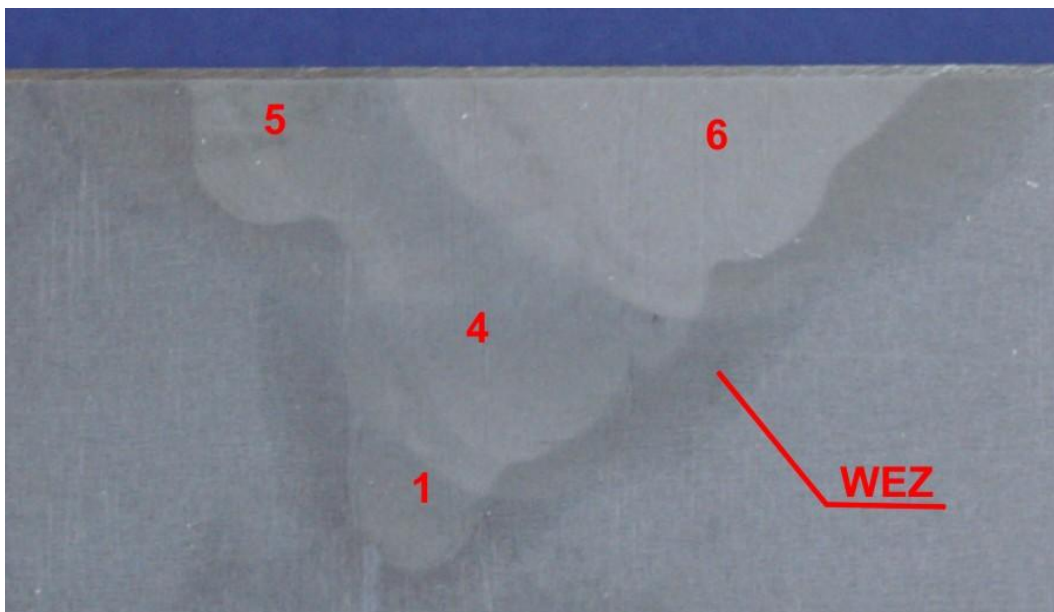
Probe 03 - Ansicht oberer Teil der Schweißnaht
